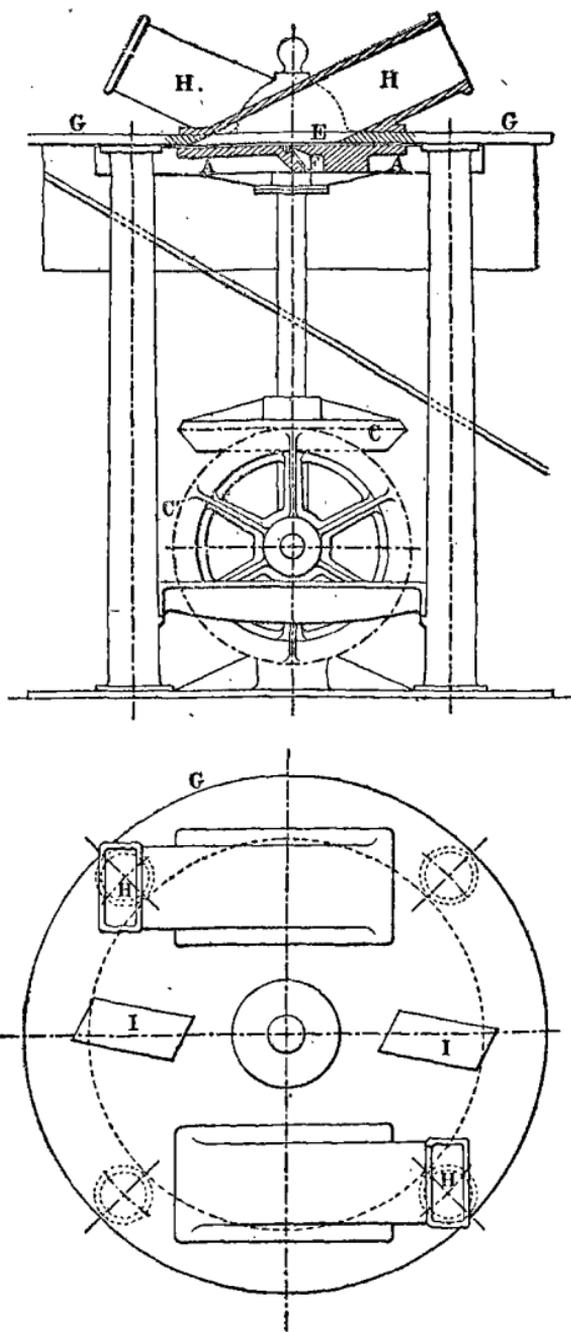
et 6f. — Machine à déchiquter de M. Cuvier fils.
